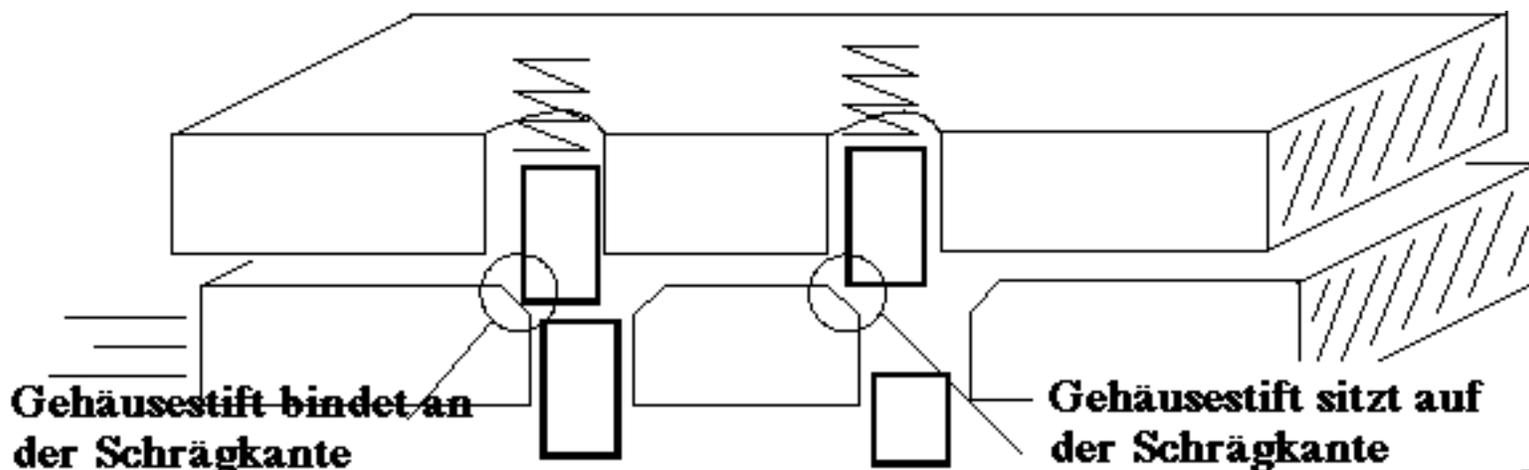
(a) Der Gehäusestift klemmt in der Schrägfläche
